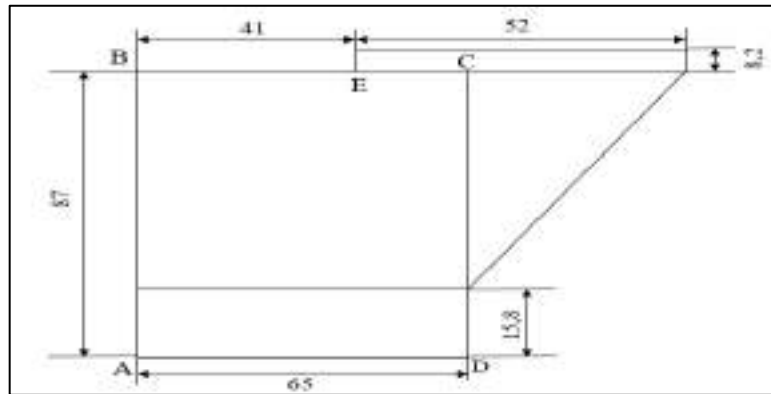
Vista lateral alámbrica estructural para cálculo de vigas.
